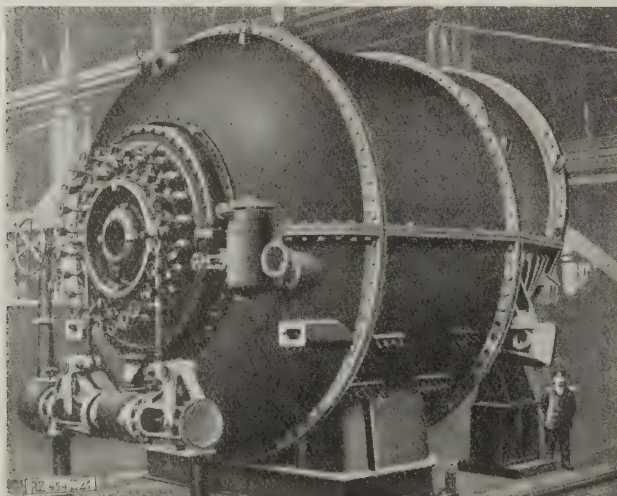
Einrad-Stirnkesselturbine für das Innwerk Töging in der Werkstatt.
